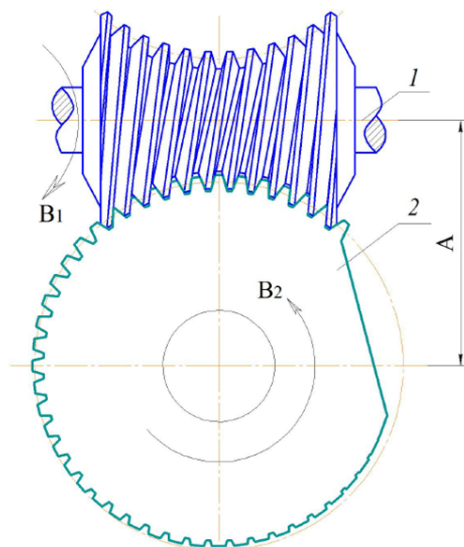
Схема многолезцовый головки для нарезания ВП глобоидного червяка по методу кругового протягивания:
